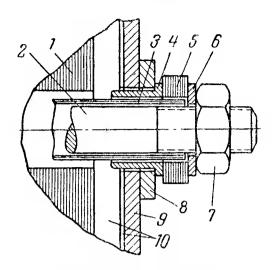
Детали прессовки ярма шпильками (усиленная конструкция).
